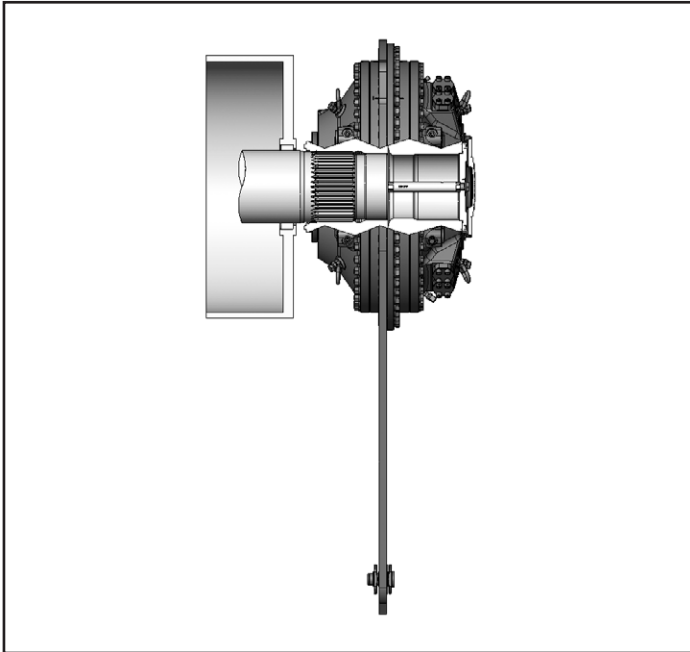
Motor mit Befestigung per Drehmomentstütze und Vielkeilverzahnung.
